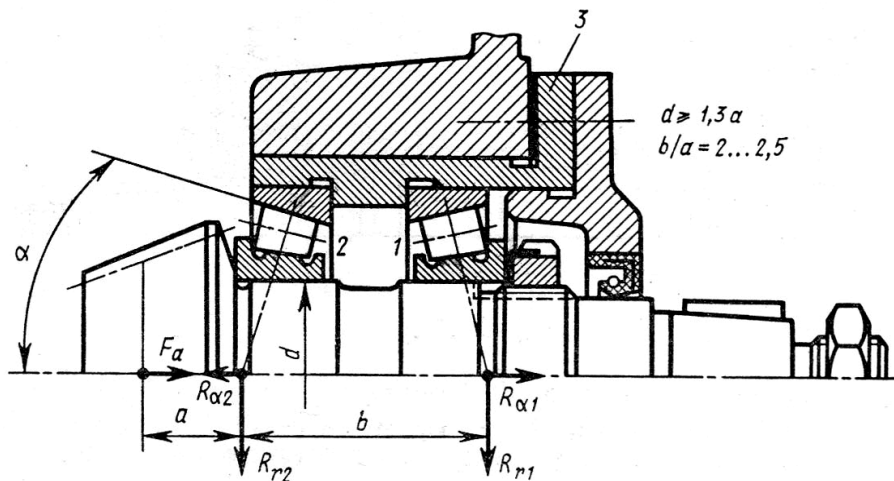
Опоры вала конической шестерни, установленные врасяжку
